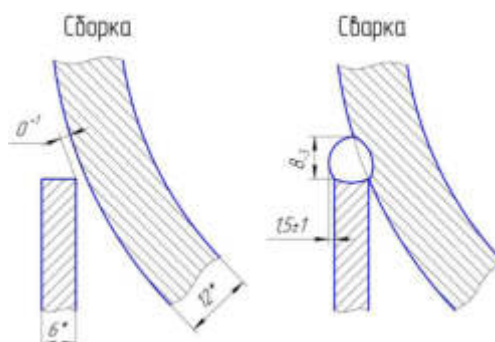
Сварной шов №2 приварки днища нижнего к обечайке опорной
